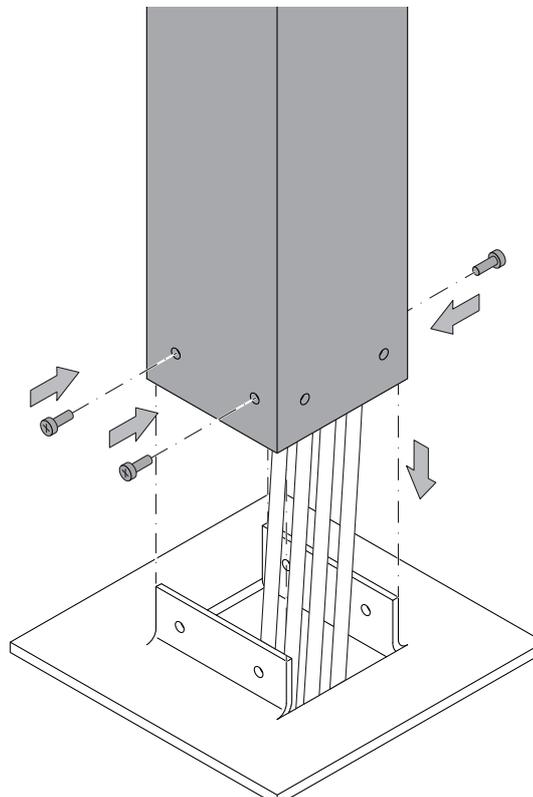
Slave-Säule mit der Bodenplatte verschrauben
